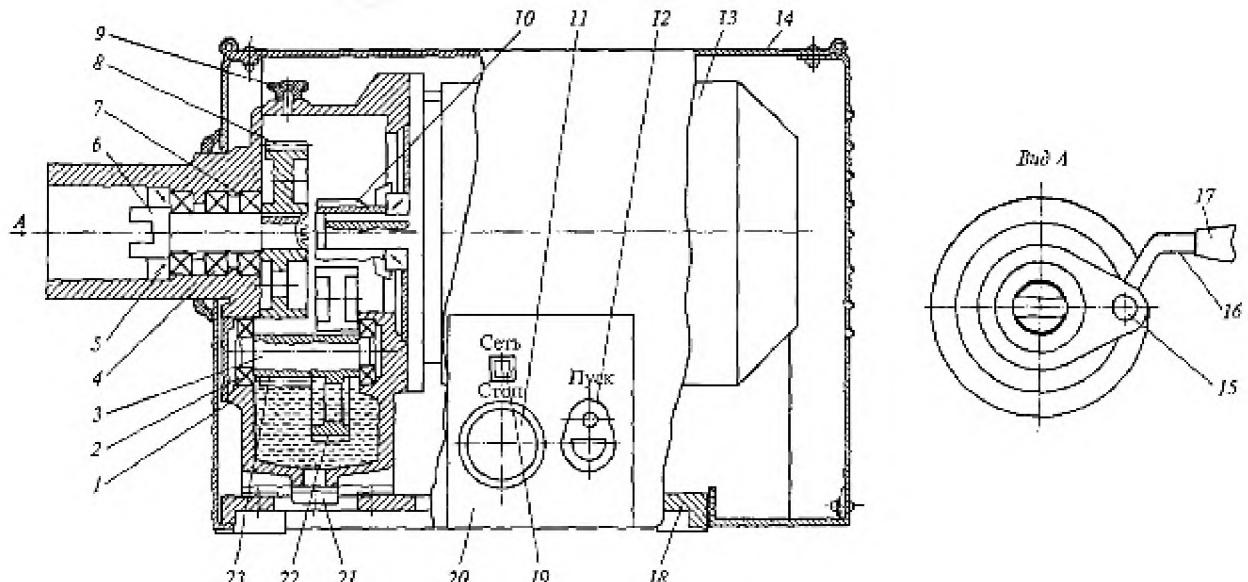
Привід ПМ: 1 – редуктор; 2, 7 – шарикопідшипники; 3 – вал; 4 – упорний підшипник; 5 – манжета; 6 – вал привідний; 8, 22 – колеса зубчасті; 9 – пробка-сапун; 10, 23 – шестерні; 11 – кнопка; 12 – перемикач або пускач; 13 – електродвигун; 14 – кішух; 15 – головка осі; 16 – кулачок; 17 – рукоятка; 18 – рама; 19 – індикатор напруги; 20 – пульт; 21 – пробка зливна
